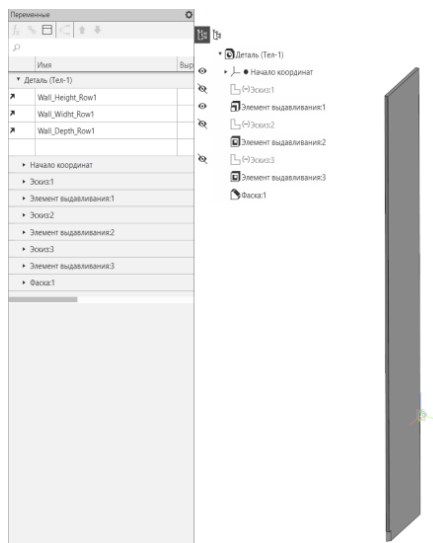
Деталь сборки «Шкаф» с назначенными параметрами
